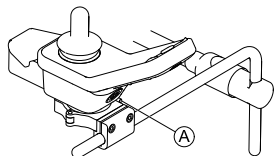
Exemple de réglage DLX-REM400. Les DLX-REM110, DLX-REM211 et DLX-REM216 sont réglés de la même manière.
